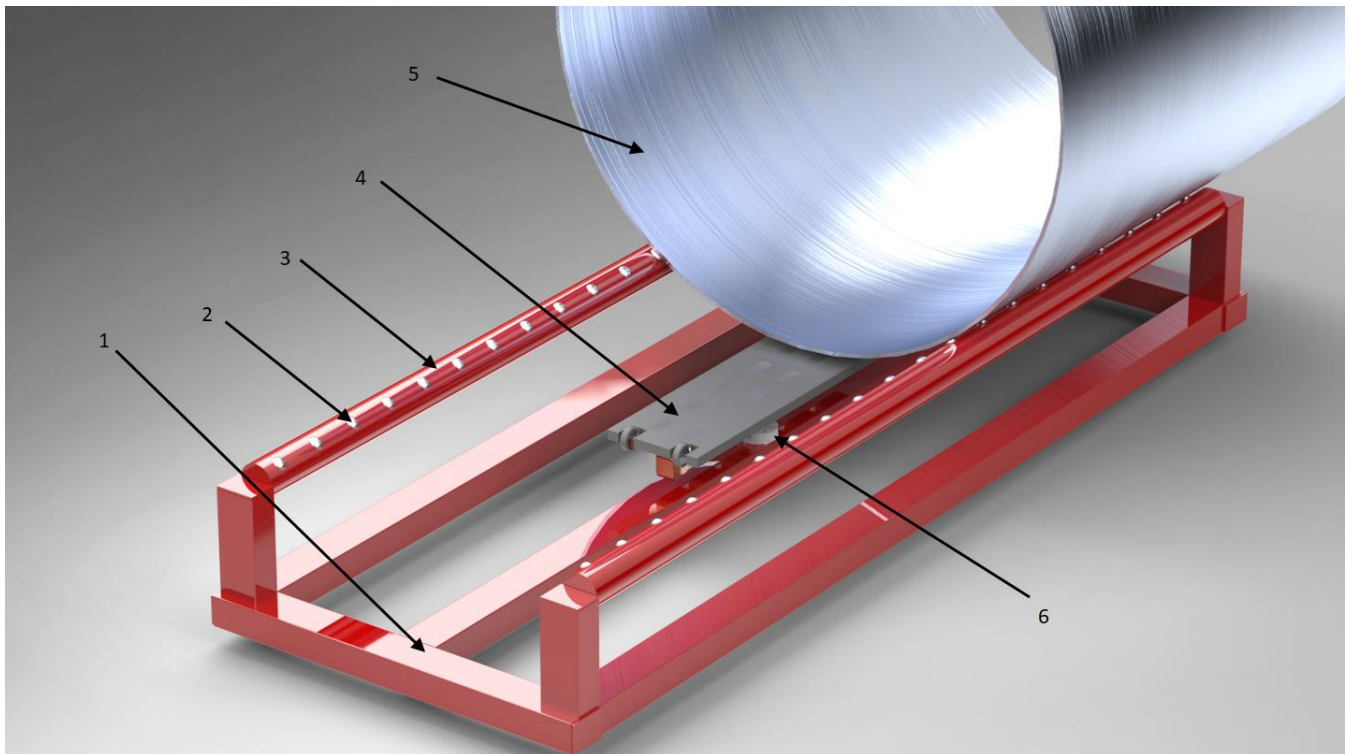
Макет стану для оперування сталевими трубами на основі модульного індуктора (1-рама, 2-шариковий ролик, 3-бокова опора з круглого профілю, 4- модульний індуктор, 5- вторинний елемент (сталева труба), 6 – трикулачковий поворотний патрон)
